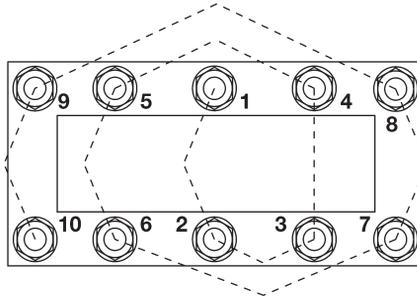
Smontaggio del gruppo meccanico di scarico
